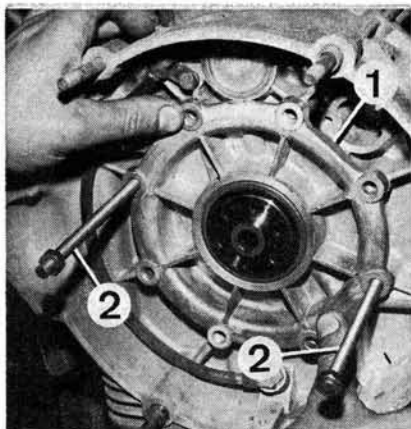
Centrage du palier arrière (Photo RMT)
